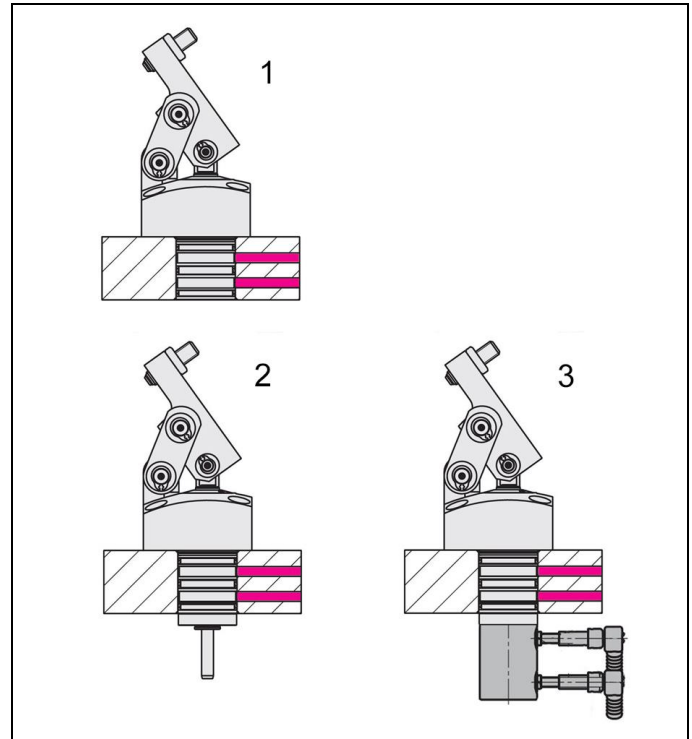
Befestigungsmöglichkeiten Einsteckausführung
